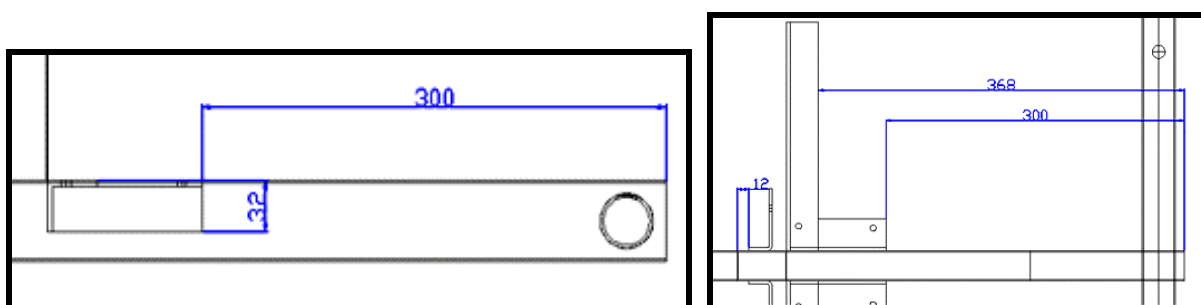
Soldar as porcas que regulam a largura do eixo traseiro.
